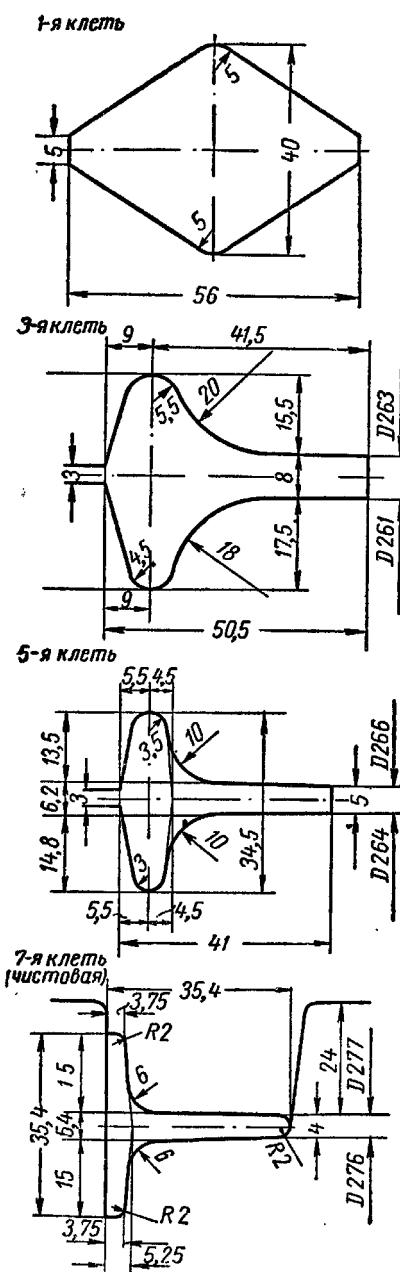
Калибровка профиля оконного переплета № 3 (ОСТ 10029—39) с пластовым расположением чистового калибра для прокатки на стане 260
